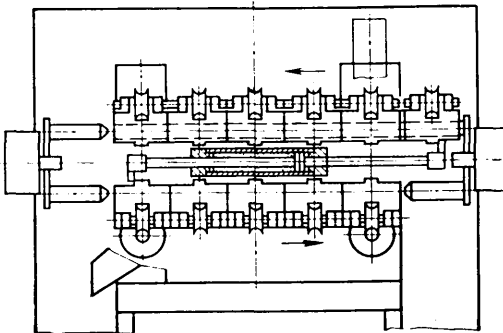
Индукционная установка для закалки и отпуска задней рессоры
